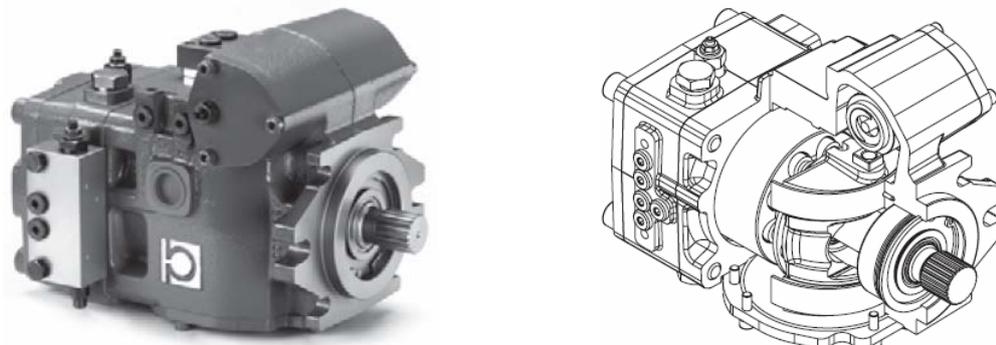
Общий вид конструкции насосов типа НР Р7 и НР Р8.
